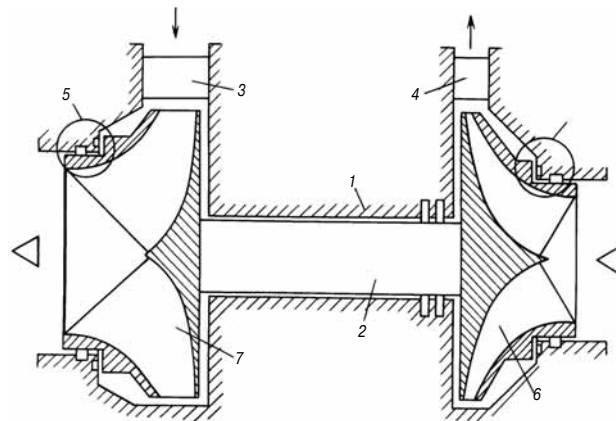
Турбокомпрессор с газостатическими подшипниками в корпусах турбины и компрессора:
